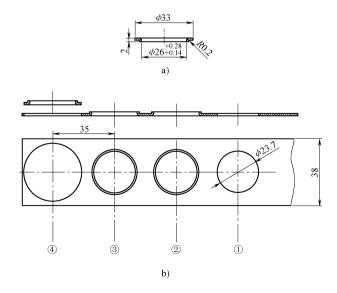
通孔凸缘级进模 a) 零件图 b) 排样图
